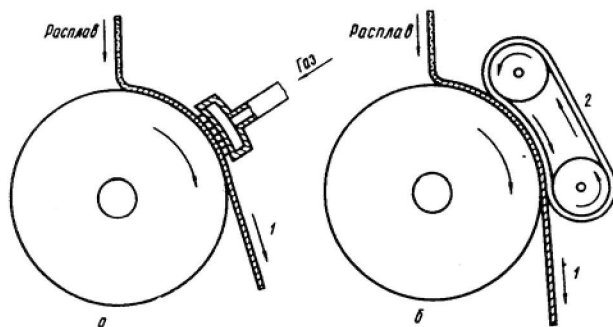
Схемы устройств для увеличения времени контакта затвердевающей ленты с диском. Использование газовой струи (а) и прижимного металлического ремня из сплава Cu – Be (б)
